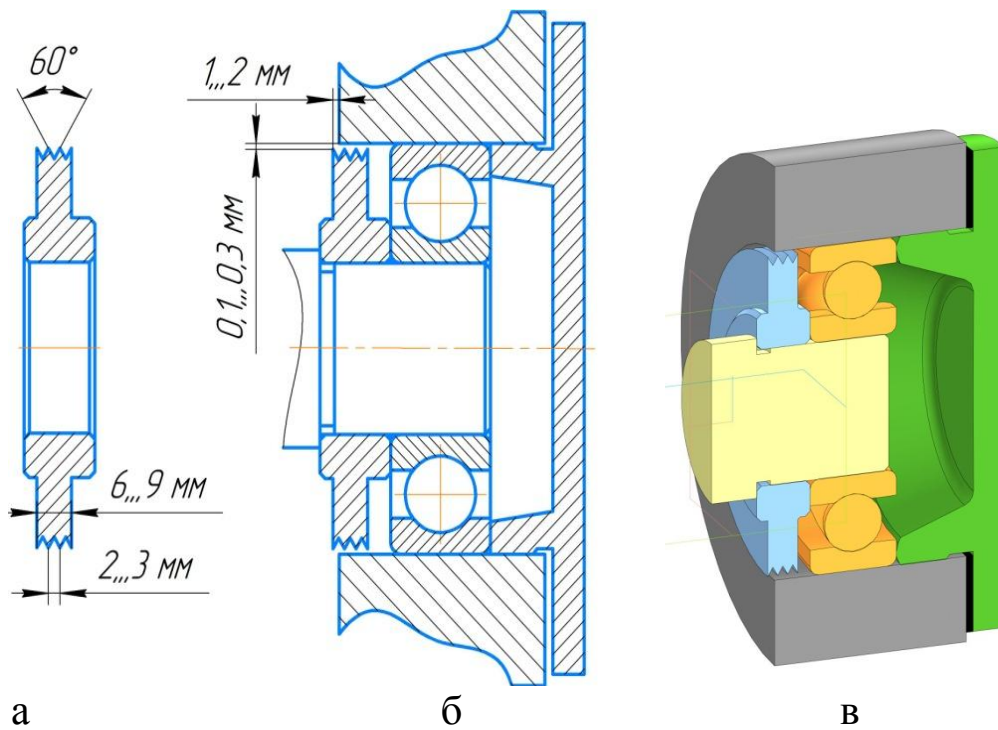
Подшипниковый узел с мазеудерживающим кольцом:
